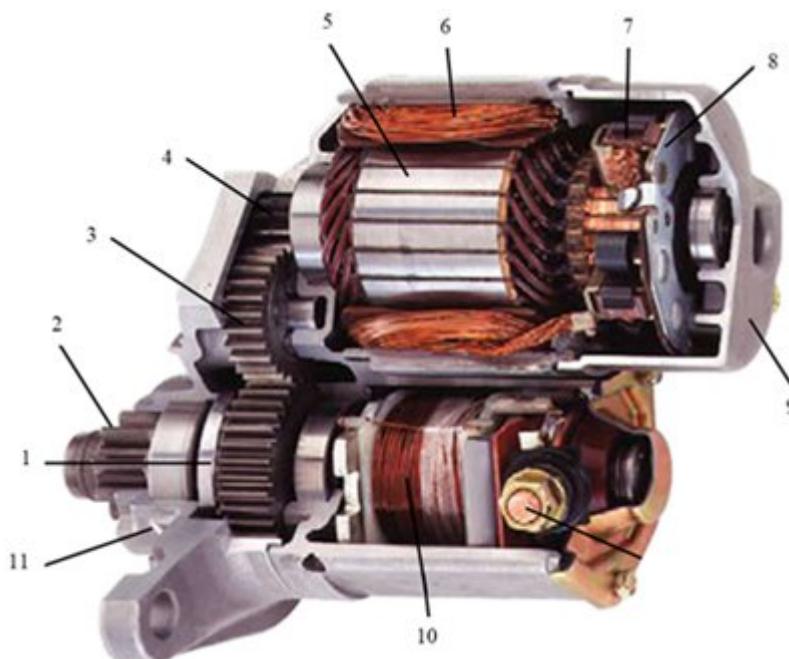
Конструкція електричного стартера із планетарним редуктором:
